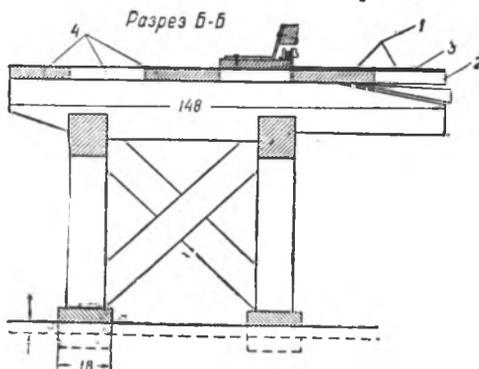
Чертеж гонторезного станка (разрез по Б—Б):
